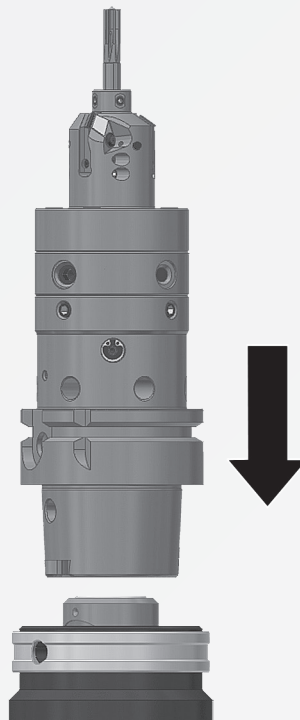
Werkzeug in Aufnahme von Einstell- oder Messgerät einspannen
